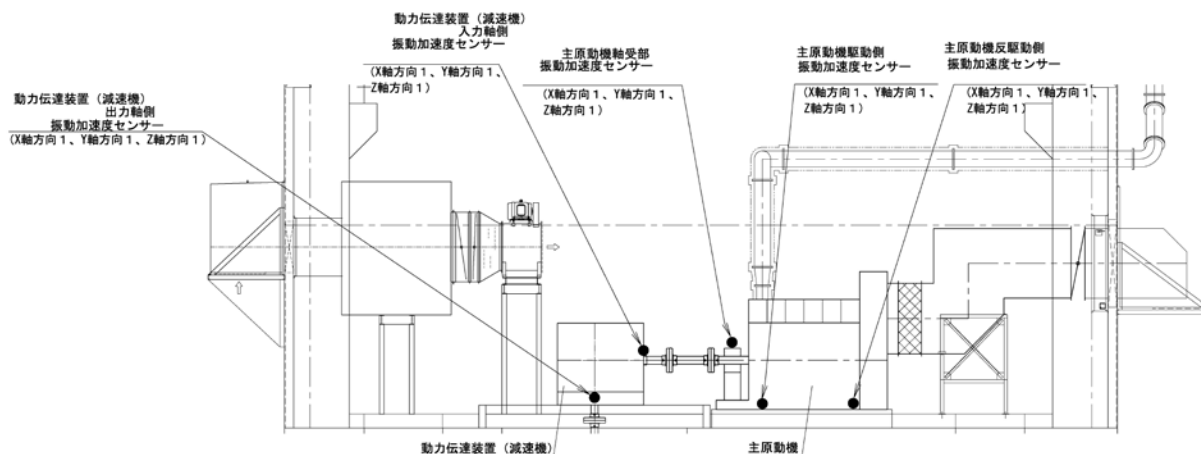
主原動機・減速機のセンサー取付位置図 (断面図)
